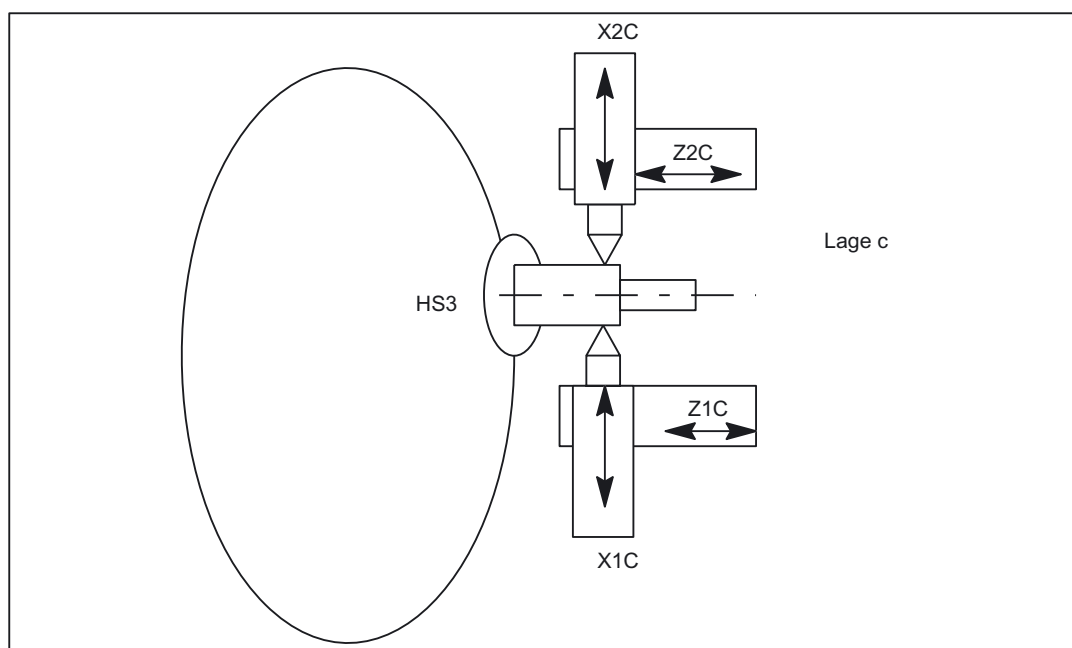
Zwei Schlitten je Lage können auch gemeinsam an einer Spindel arbeiten.
